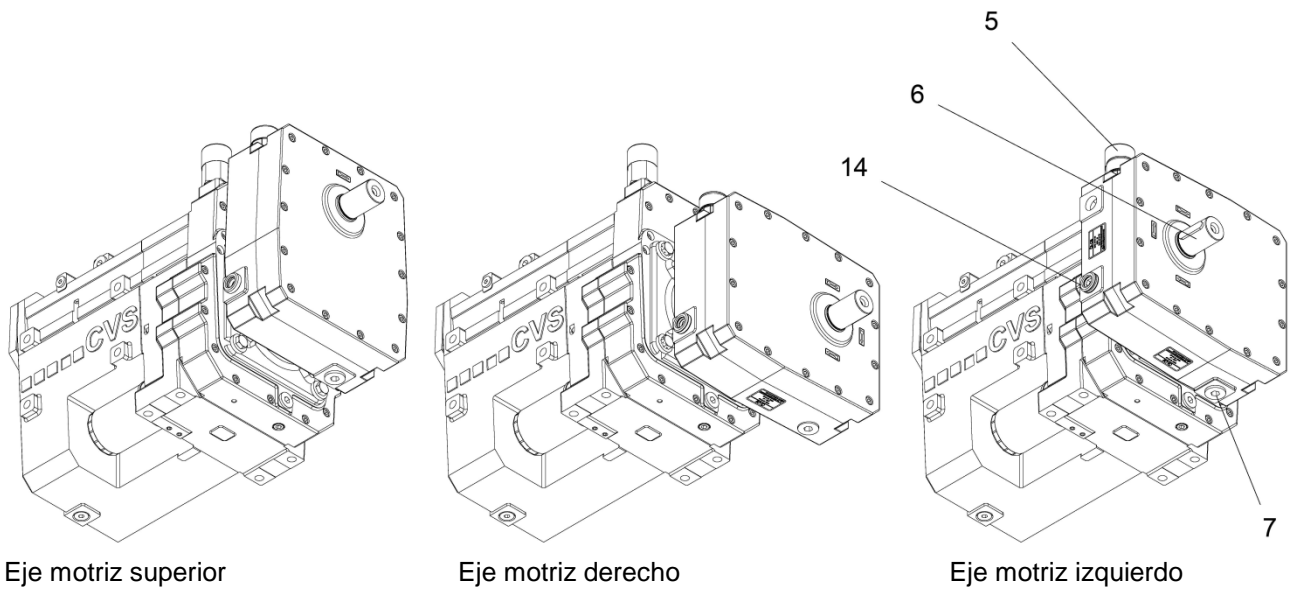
Vista del SiloKing modelo LS con engranajes adicionales
